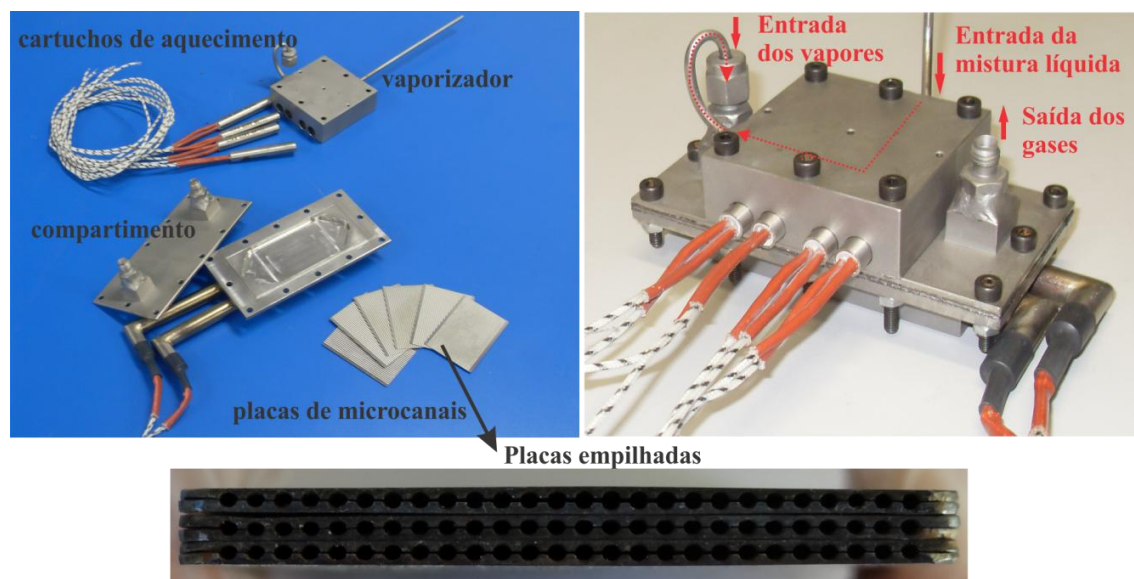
Conjunto total do microrreator fabricado pelos métodos de usinagem mecânica e corrosão química.
